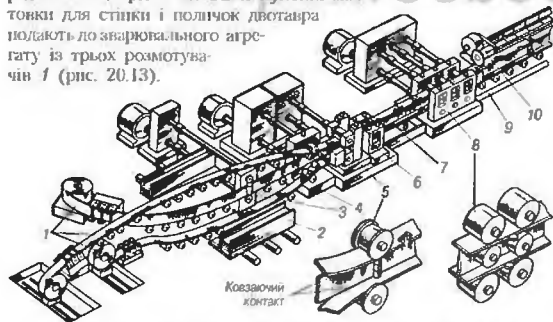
Схема агрегату для виготовлення двотаврових профілів зварюванням СВЧ:
